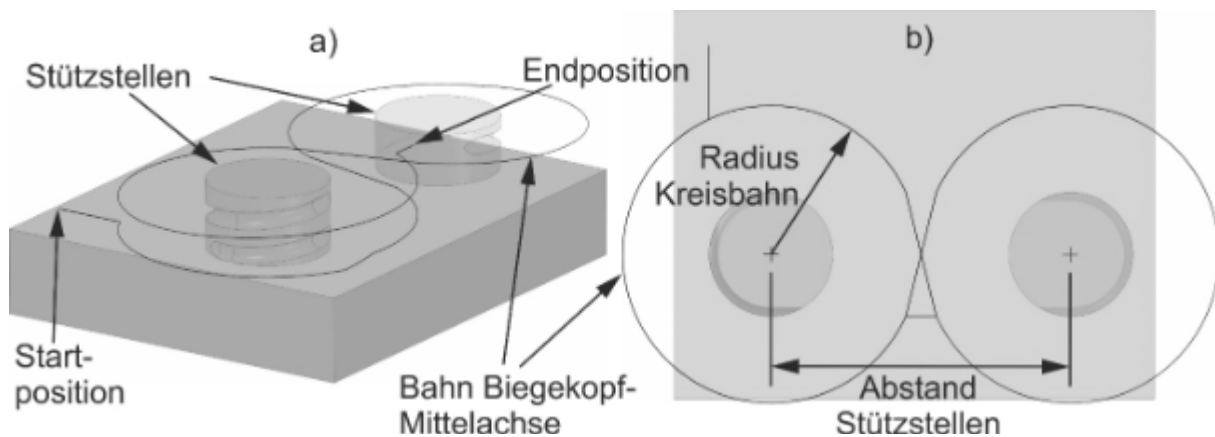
3D Geometriepanung: a) 3D-Ansicht, b) Draufsicht
